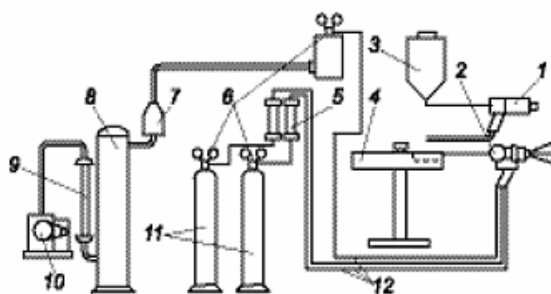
Схема установки для сверхзвукового газопламенного напыления
